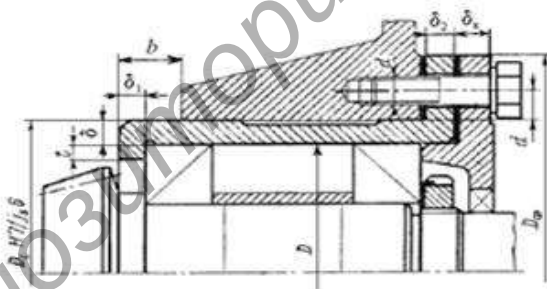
Конструкция стакана для фиксирующих опор или опор конических зубчатых колес
